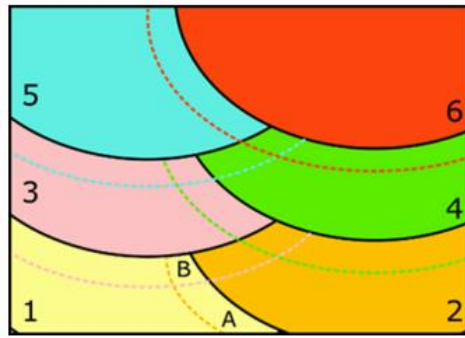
Representação esquemática de 6 passes de soldadura [29]
